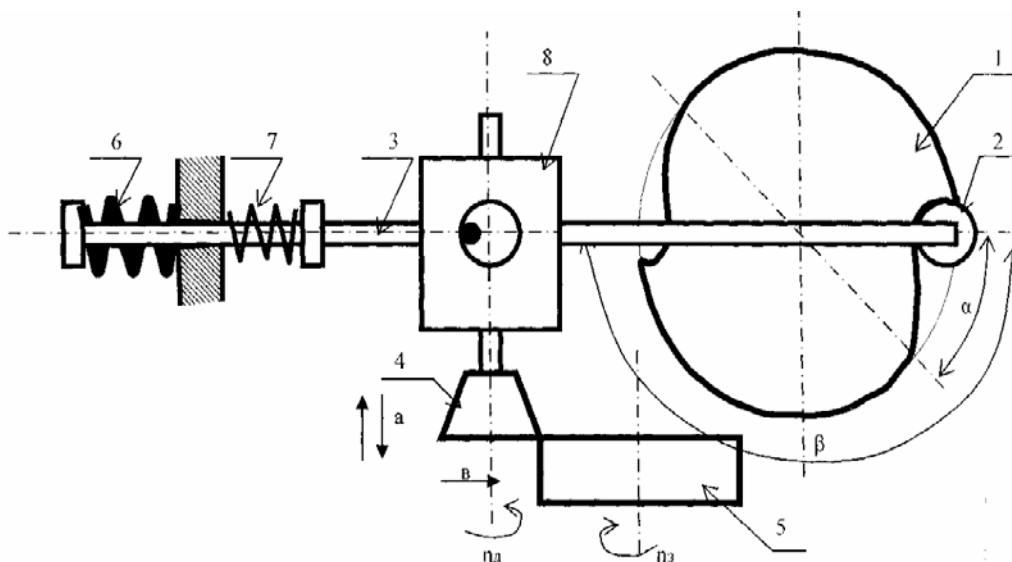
Схема обеспечения врезания и круговой обкатки при зубодолблении заготовки
